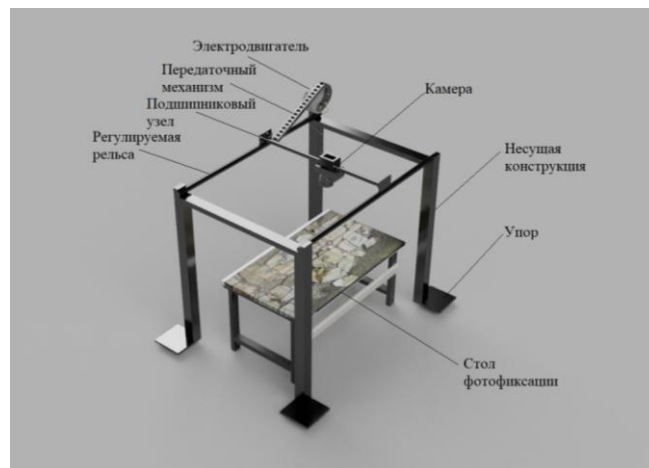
Прототип приспособления для получения цифровых изображений фресок
